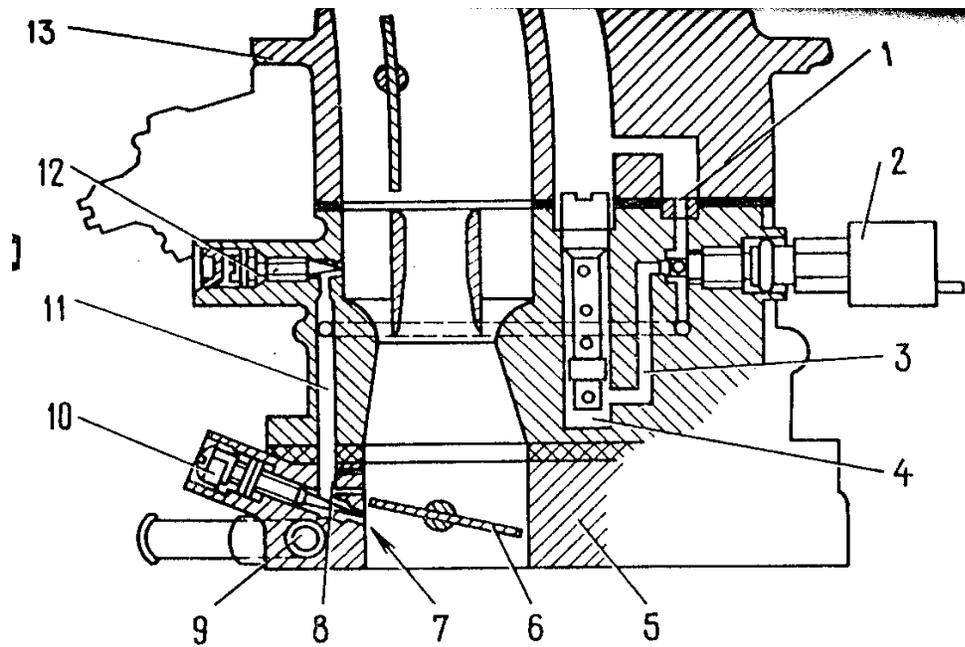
Esquema del sistema de ralentí del carburador 2106-1107010:
